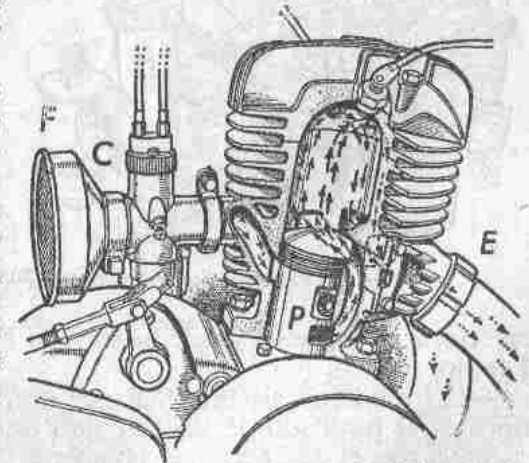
El motor D. K. W. cortado; F, filtro del aire; C, carburador; P, pistón; E, escape.
